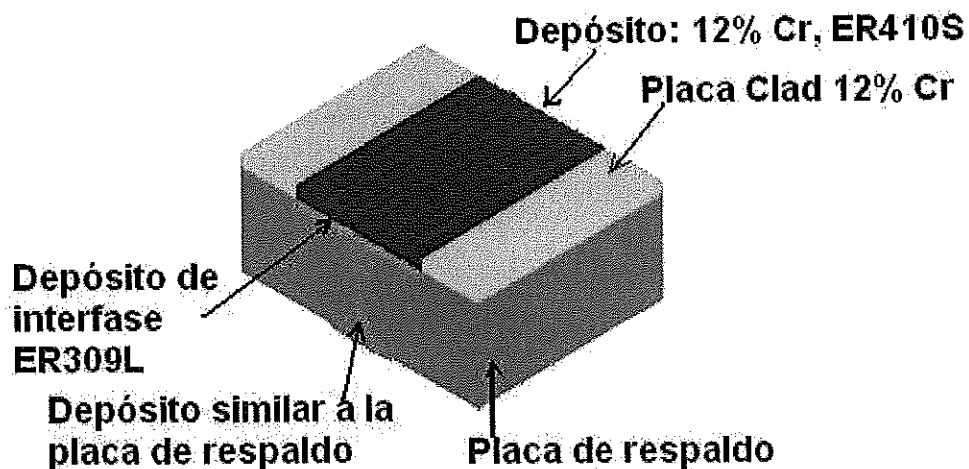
Junta de soldadura de placa clad.
